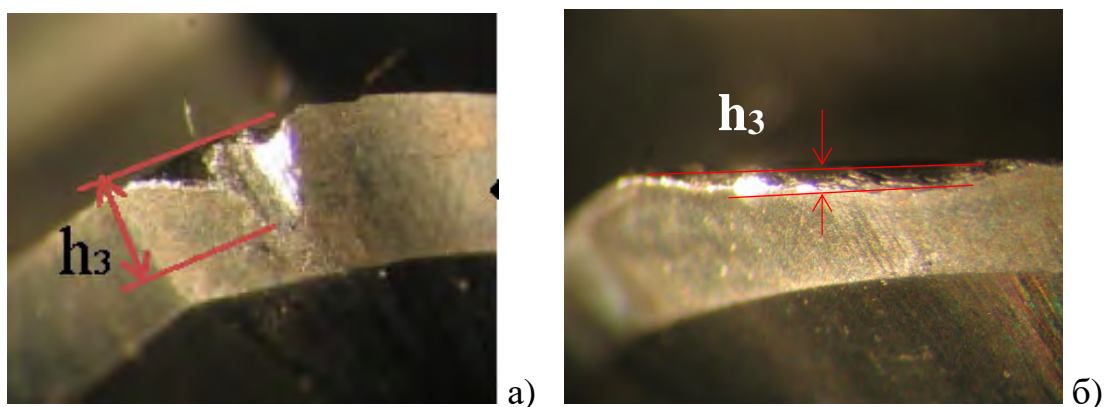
Характер разрушения твердосплавной фрезы при черновом фрезеровании титанового сплава: а – без покрытия; б – с дискретным оксидным слоем
